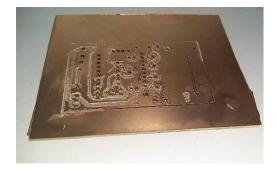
Router CNC Cyclone PCB Factory fresando a peça. Fonte: Imagem do autor.
